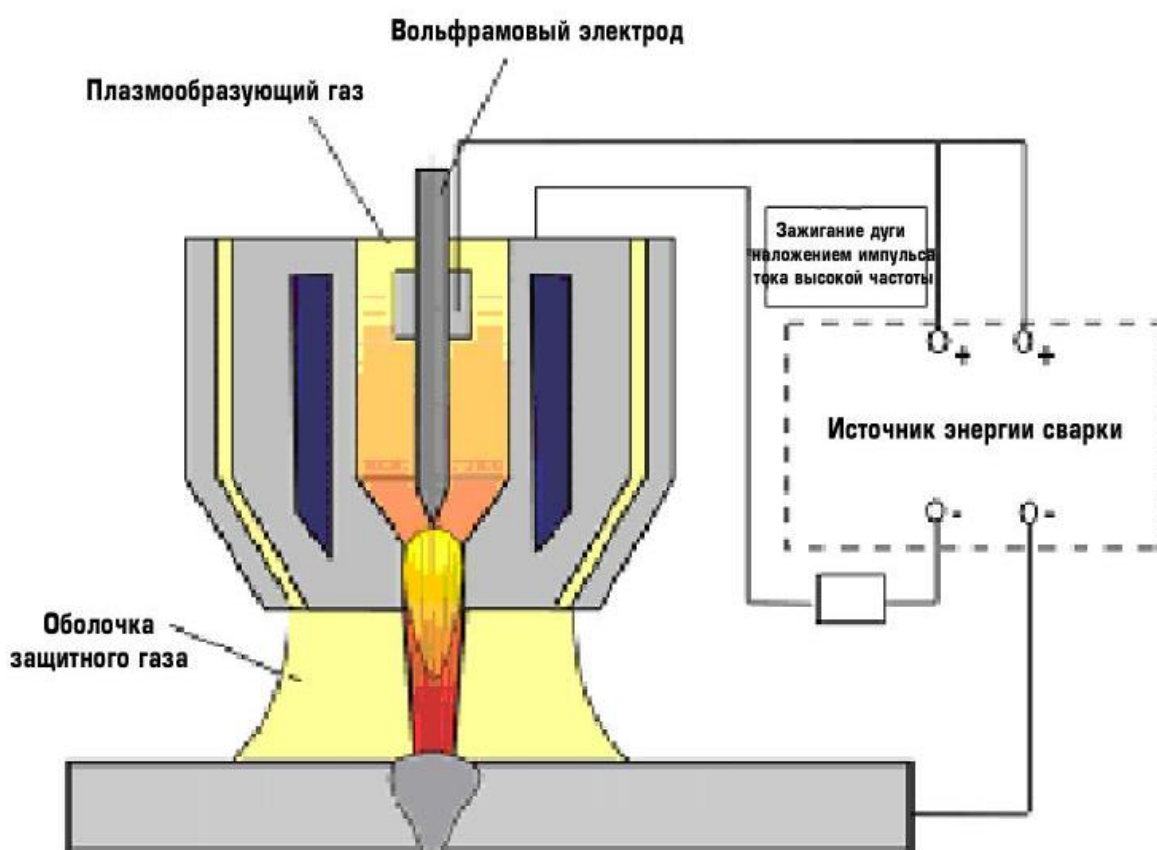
Схема процесса сварки сжатой дугой
